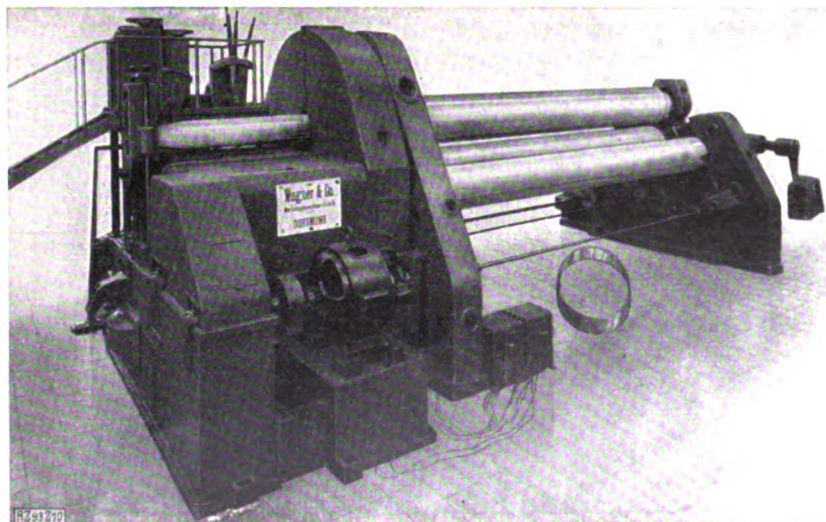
Vierwalzen-Blechbiegemaschine mit Reibwendegetriebe (Wagner & Co.).
